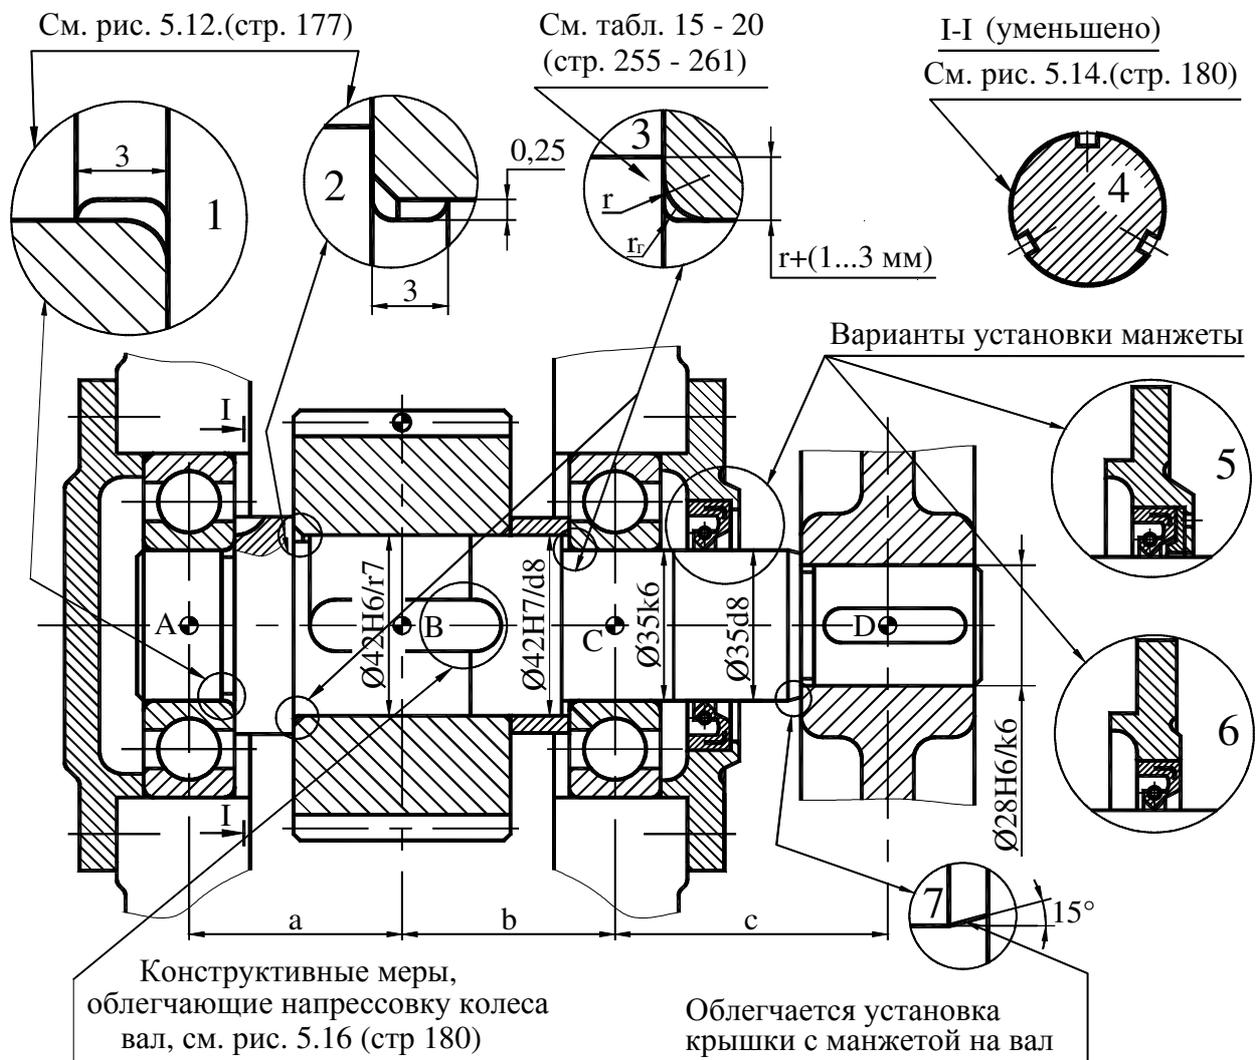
Пример конструкции входного вала редуктора одноступенчатого цилиндрического редуктора
